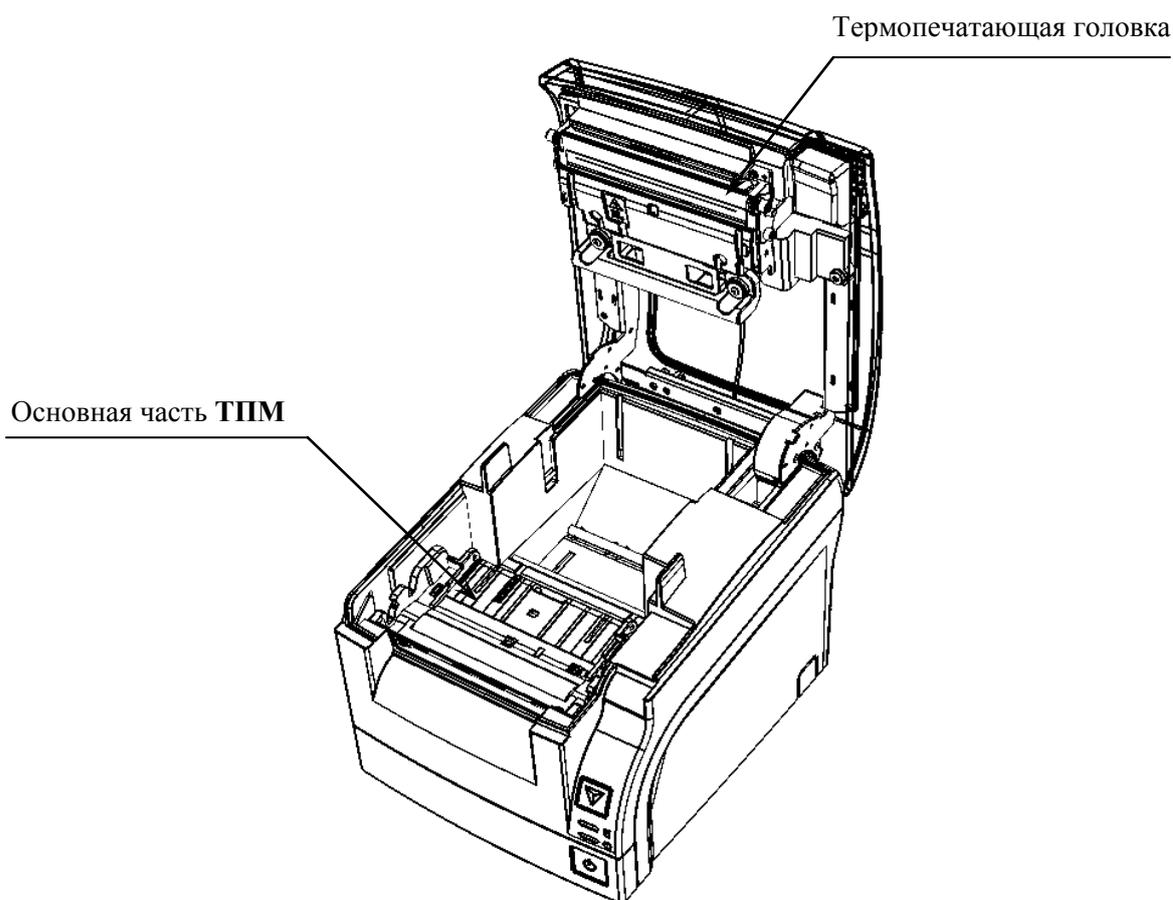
Расположение составляющих частей ТПМ в корпусе изделия.
